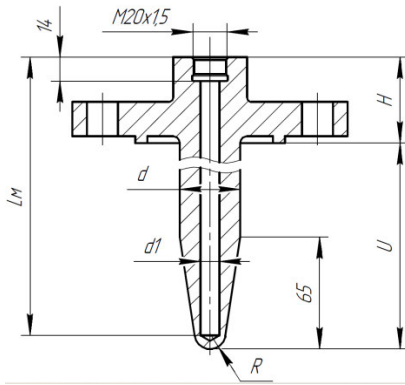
ГТ-714 для ДТ с неподвижным штуцером
